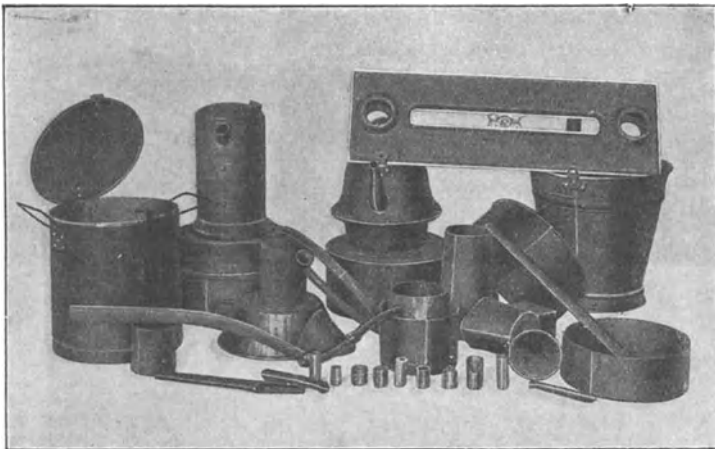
Beispiele von Nahtschweißungen.
